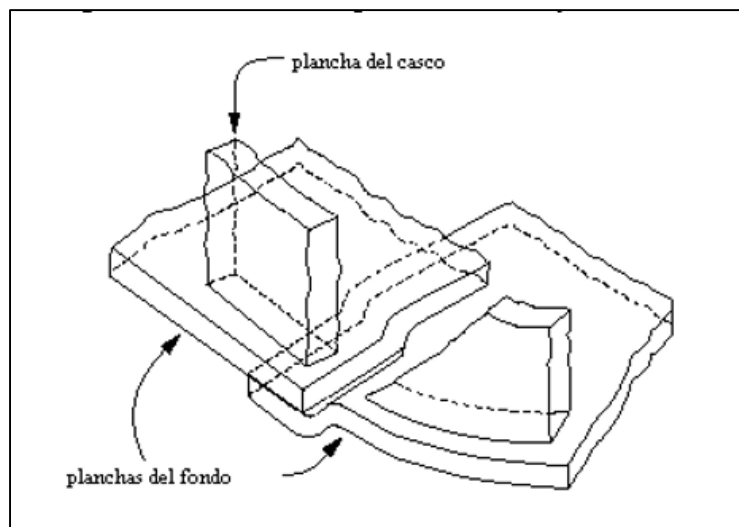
Método para preparación de planchas de fondo soldadas a solapa Debajo del casco del tanque
